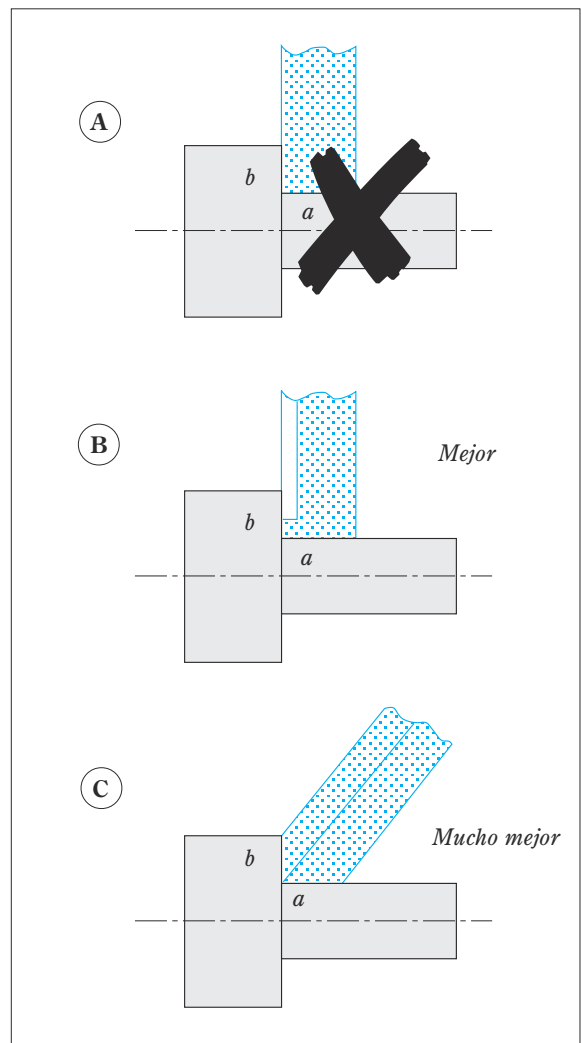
Un rectificado incorrecto puede conllevar normalmente grietas de rectificado.
